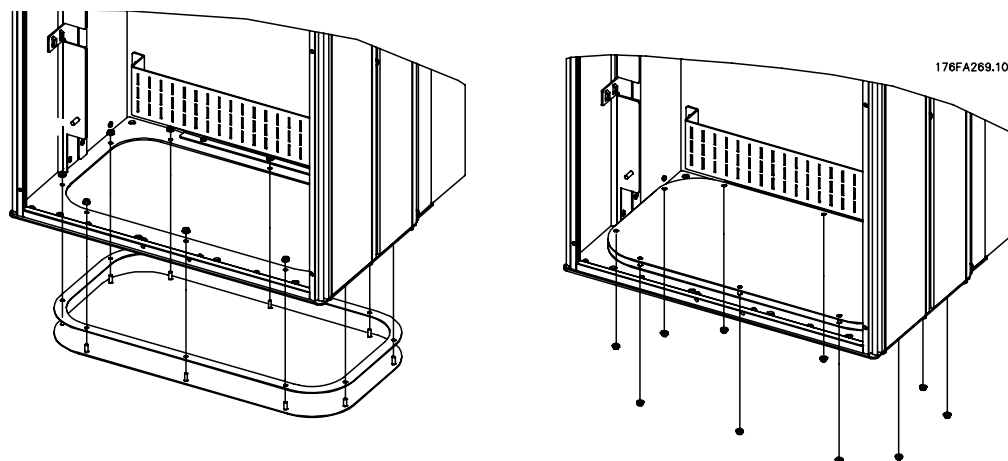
Монтаж нижней платы, Размер корпуса E1.
